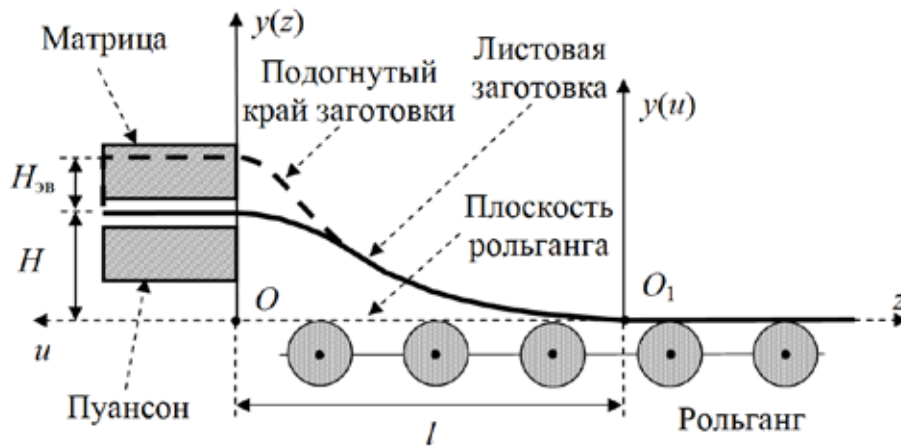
Форма продольной кромки листовой заготовки на КГП
